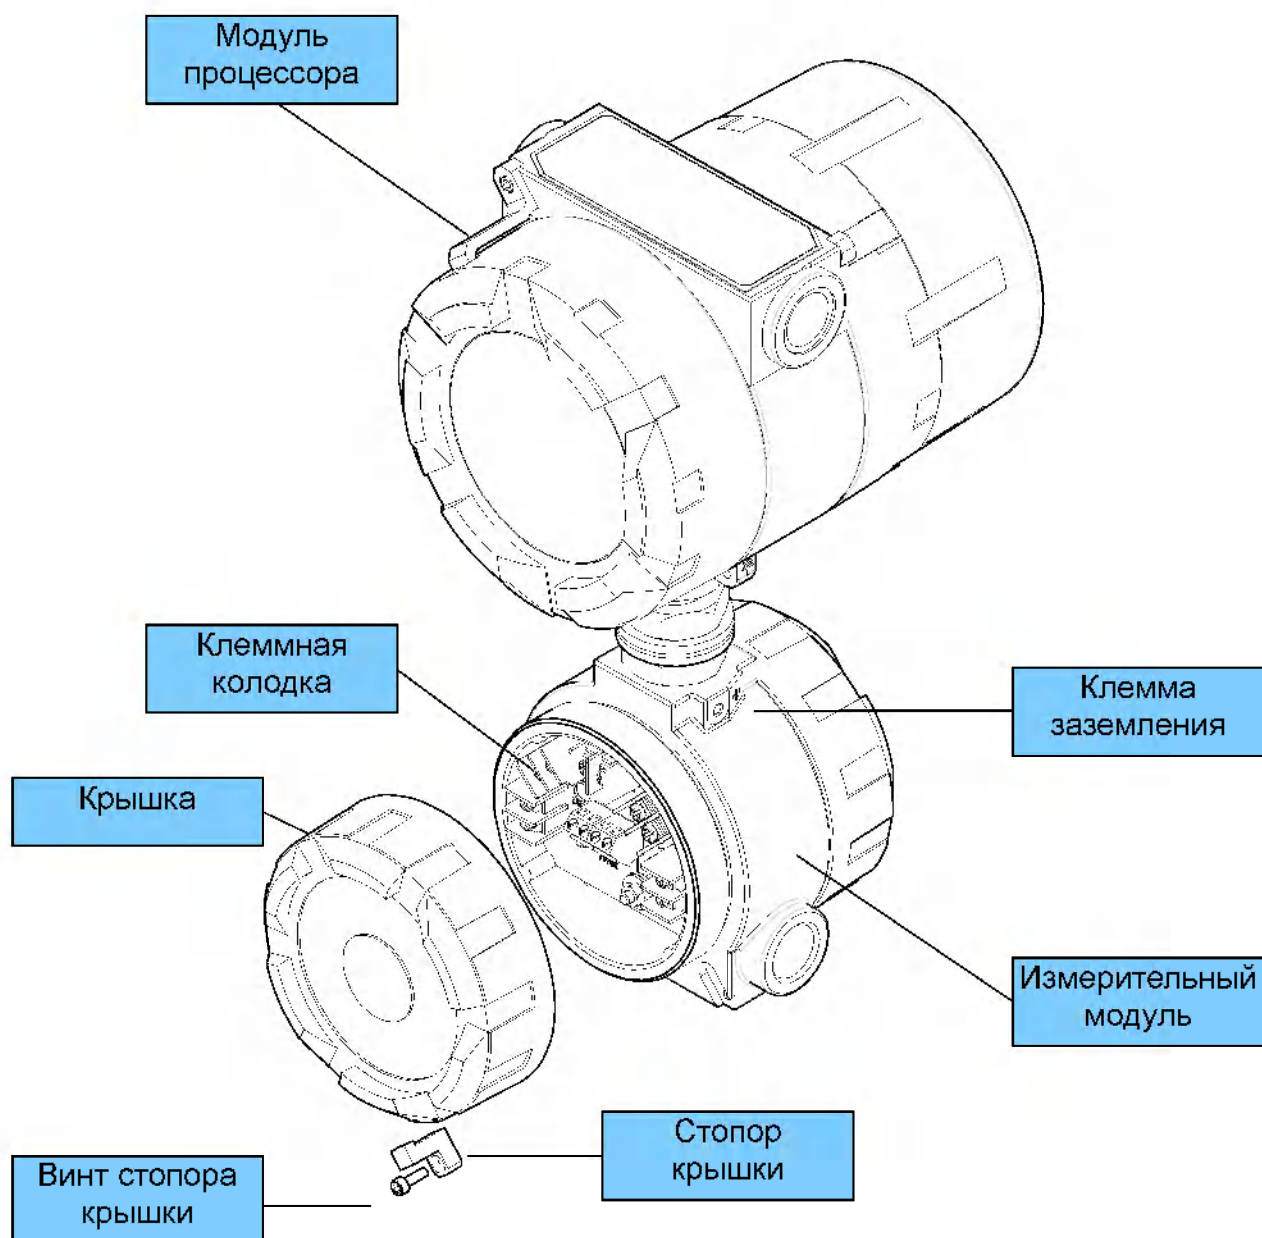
Корпус измерительного модуля (исполнение Р)
